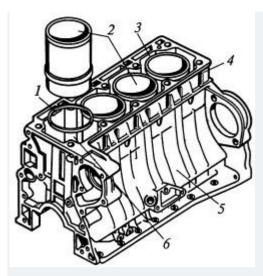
Блок двигателя со съемными гильзами цилиндров
